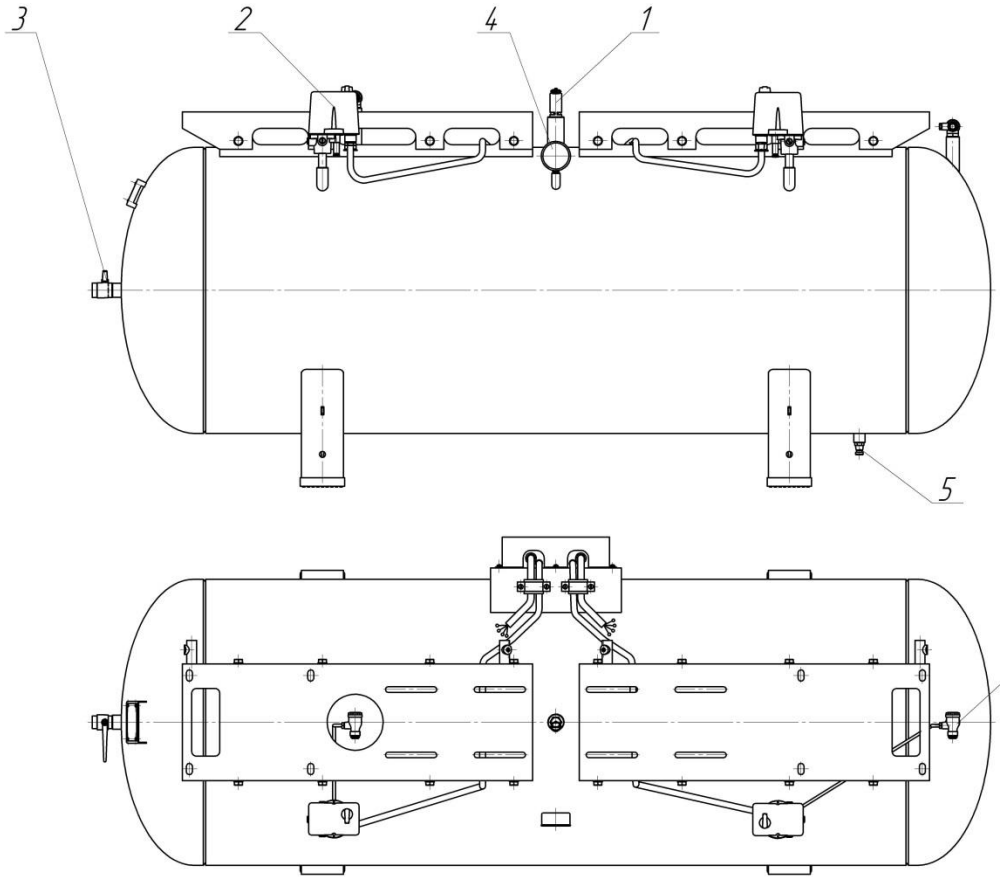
Резервуар установки компрессорной, модель К-3:
